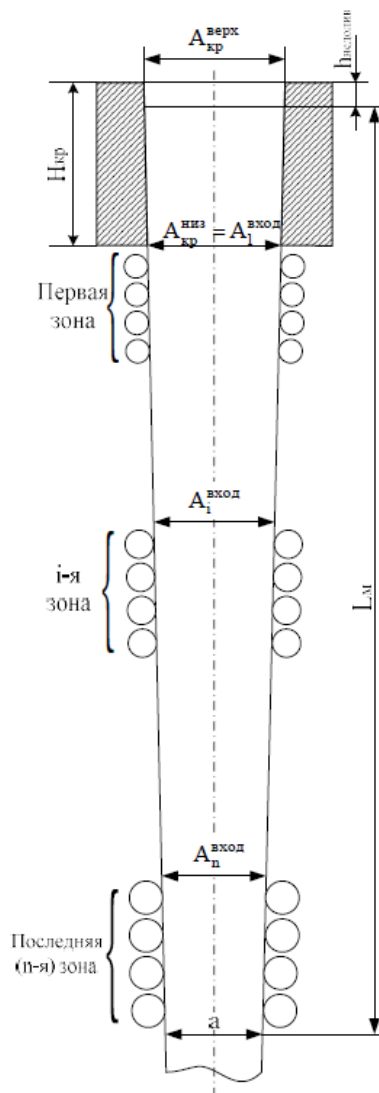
Схема настройки МНЛЗ по толщине заготовки
